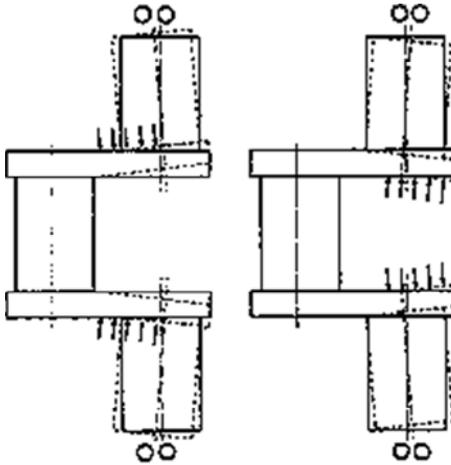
Схема правки коленчатого вала наклепом щек
